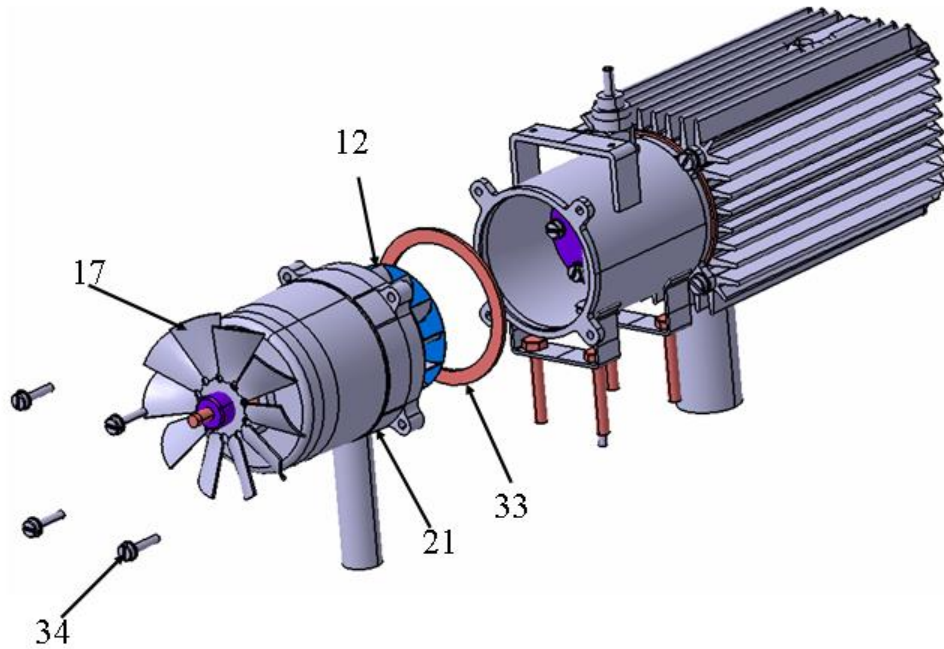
b Desen subansamblu grup motor, arzător, schimbător de căldură 3D explodat
